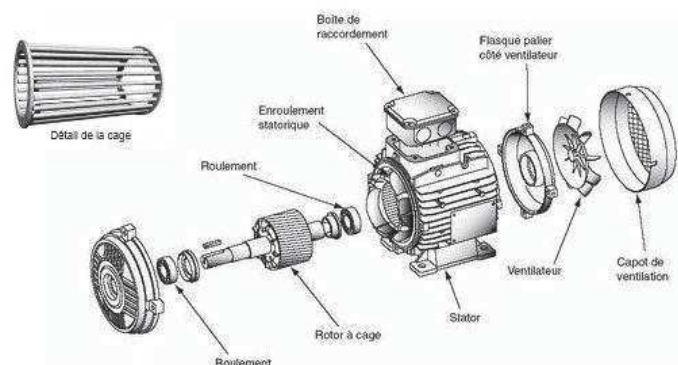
5. Vue éclatée d'une machine asynchrone à cage [5].
